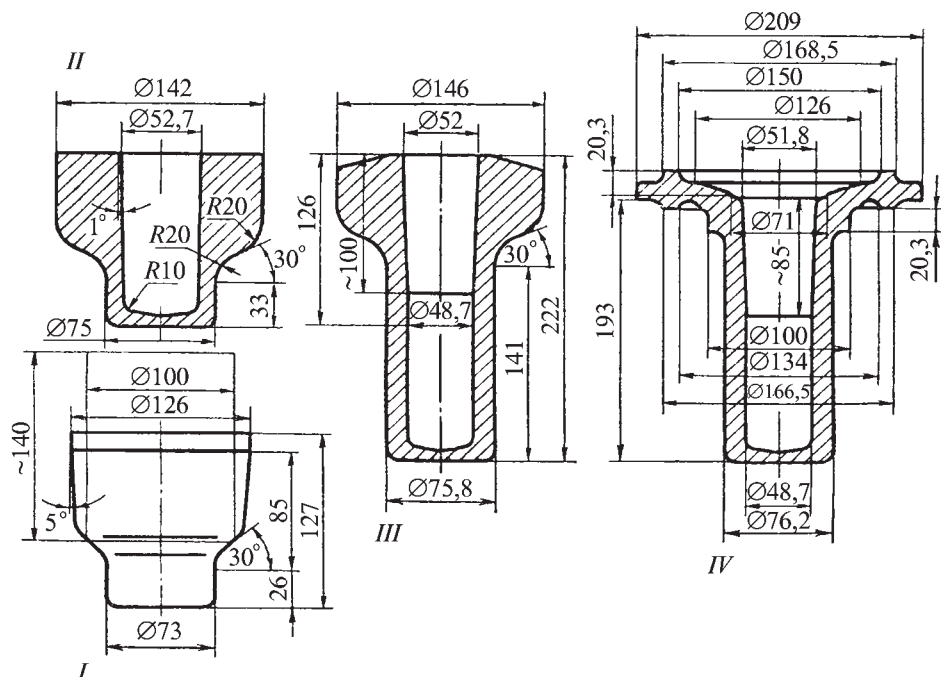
Четырехпереходная штамповка поковки с глухой полостью:
